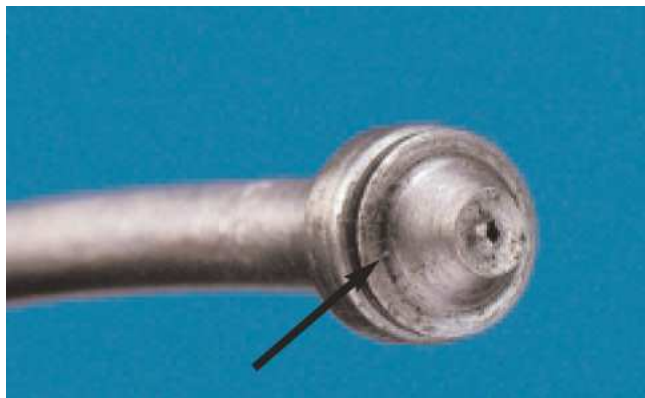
Casquillo roto de la tubería de combustible
